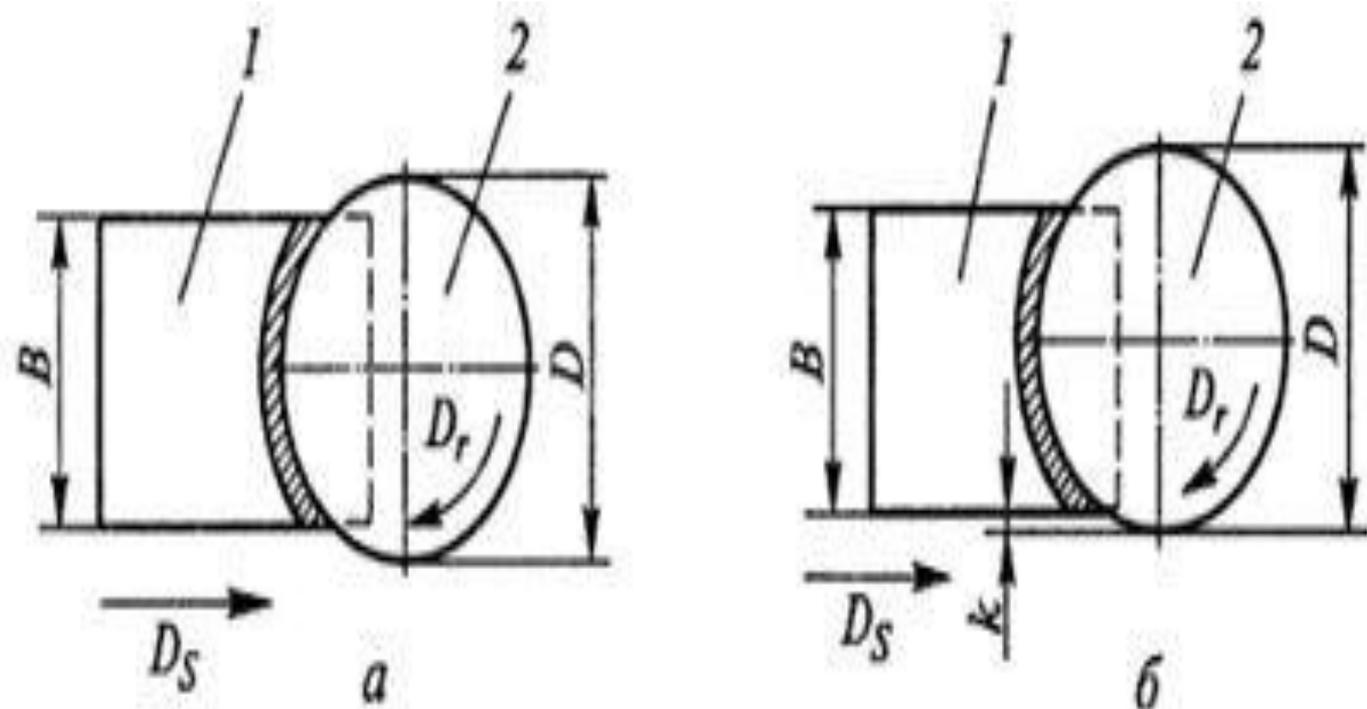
Установка торцевой фрезы относительно заготовки:
